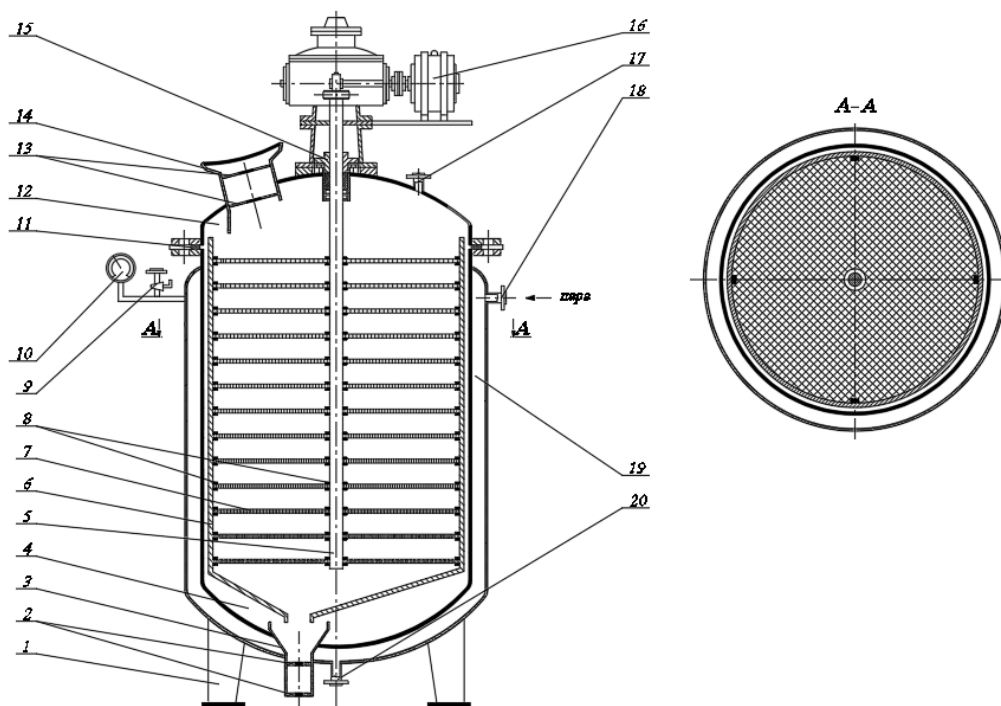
Вібраційна вакуумна сушарка безперервної дії для сушіння овочевої сировини: 1 – опори; 2 – запірний клапан; 3 – горловина; 4 – робоча камера; 5 – робочий вал; 6 – корпус для лотків; 7 – лотки для продукту; 8 – кріпильні елементи; 9 – клапан для видалення надлишкового повітря; 10 – манометр; 11 – затискач; 12 – кришка апарату; 13 – дозуючий клапан; 14 – завантажувальний бункер; 15 – ущільнювач для герметизації; 16 – віброгенератор; 17 – патрубок для видалення повітря; 18 – патрубок для подачі теплоносія; 19 – парова оболонка; 20 – патрубок для зливу теплоносія
